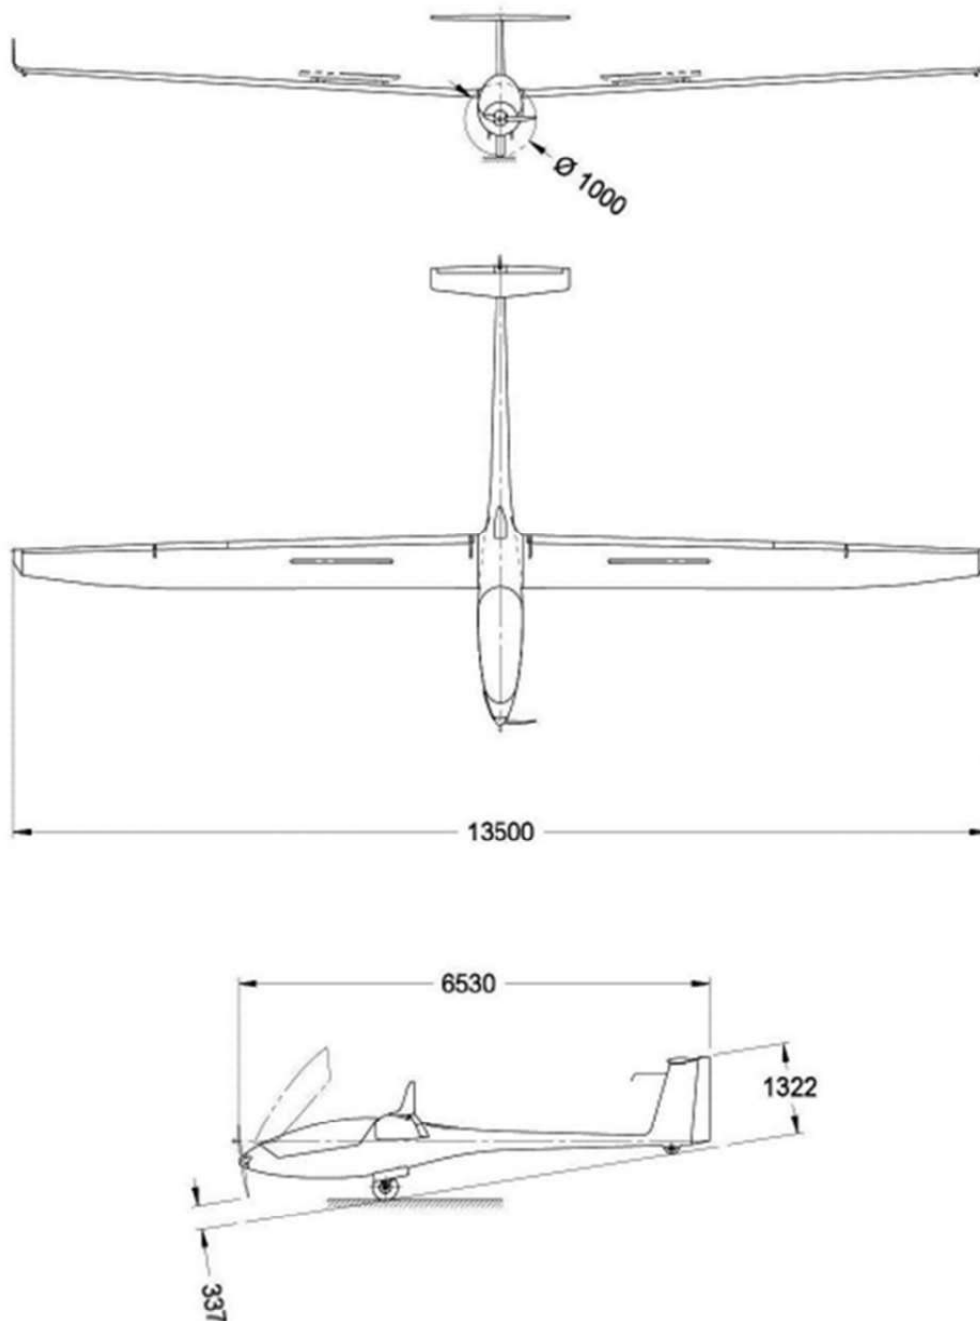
Drei-Seitenansicht des Motorsegler LAK-17B FES mini (Maßangaben in mm) Quelle: Hersteller
